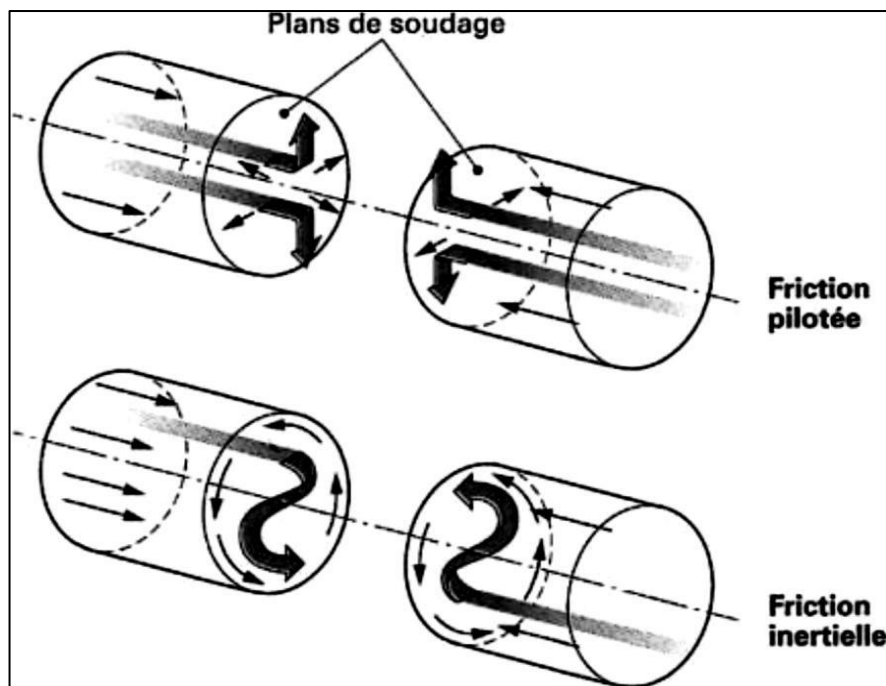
Torsion des fibres en soudage par friction [5]
